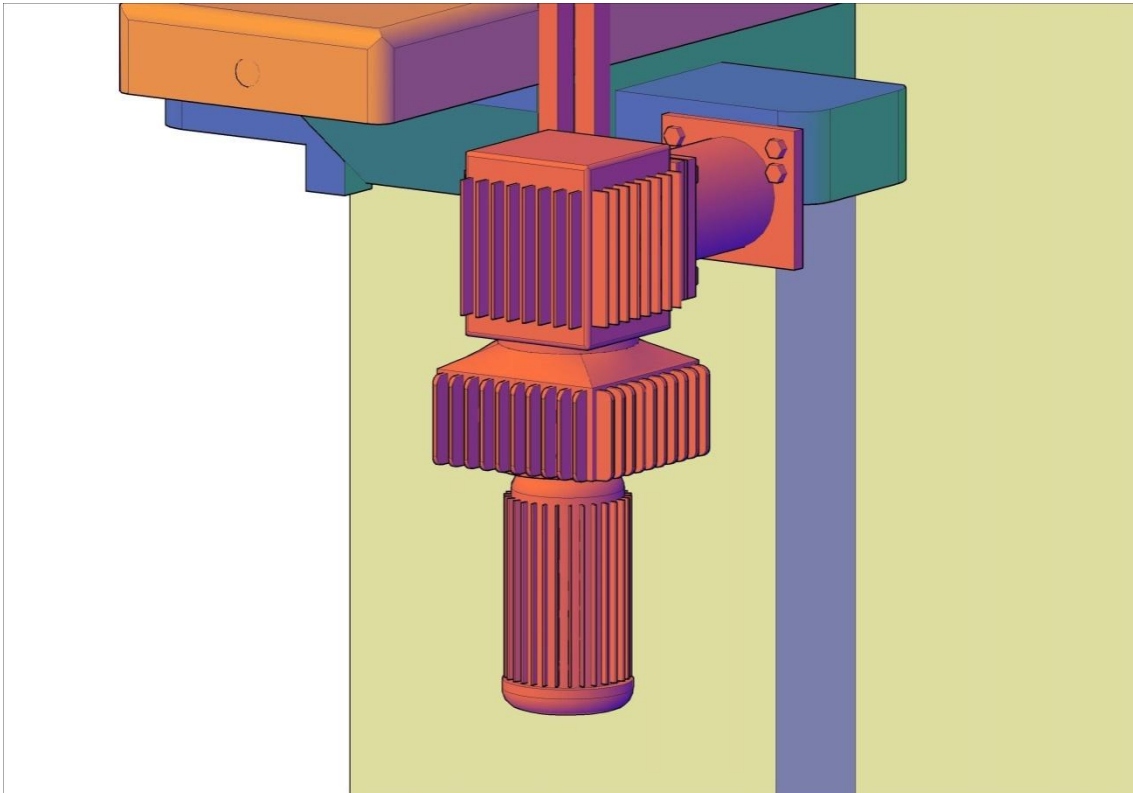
Conjunto Motor, moto-reductor e reductor redução 1:80.
